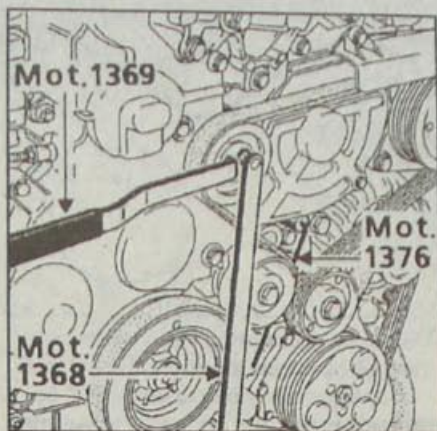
Установка приспособлений Mot. 1368, Mot. 1369 и Mot. 1376 для снятия эксцентрикового регулировочного ролика
